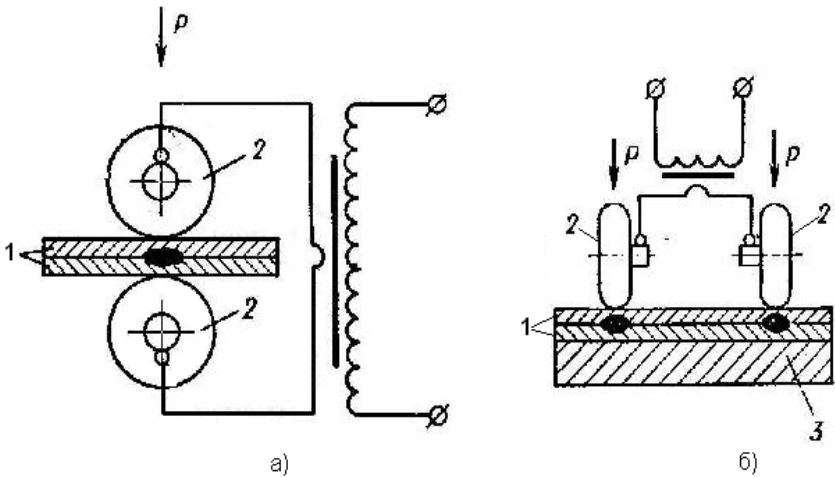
Принципиальная схема шовной сварки:
